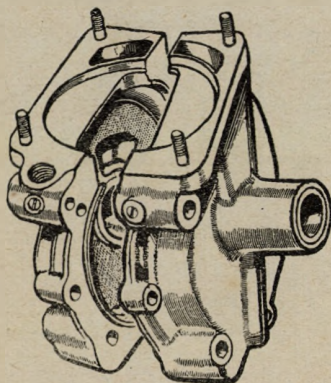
Kontrola vnitřku motoru „Bradshaw“ zrcadlem.
